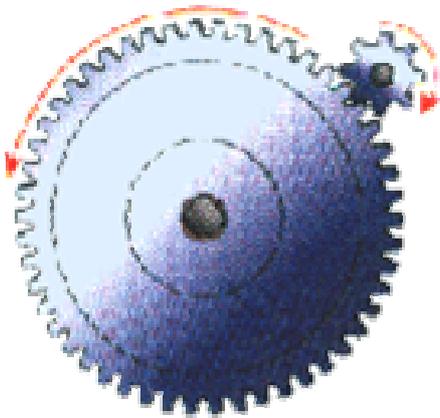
19. Engranaje de ruedas rectas a engranaje plano.
